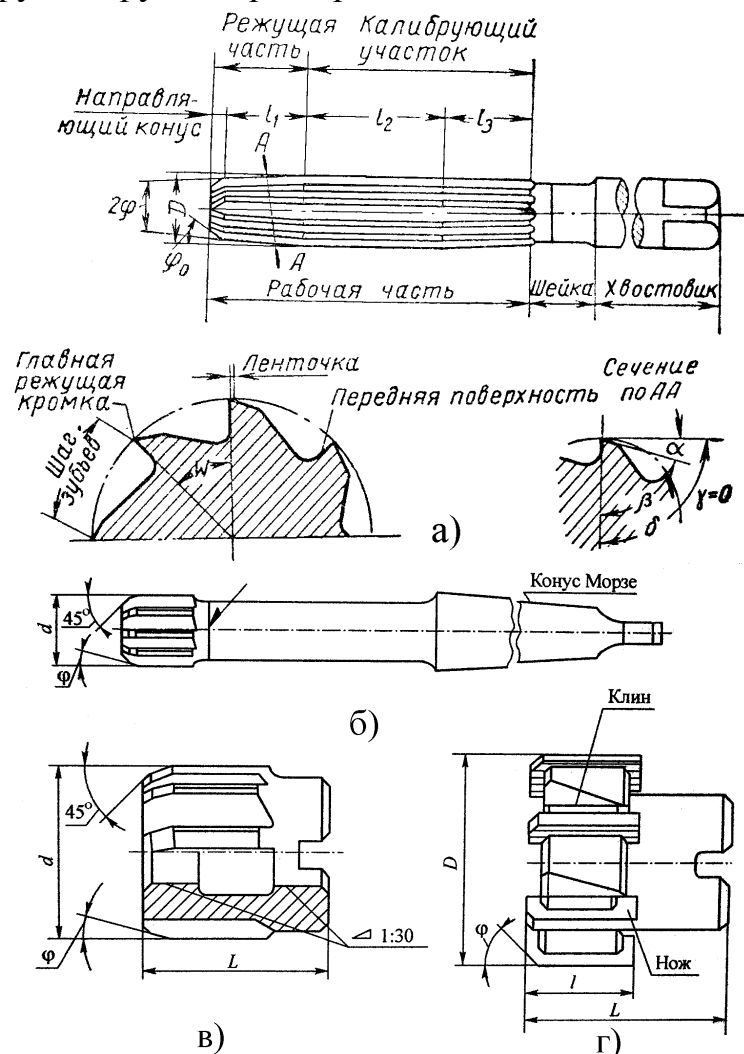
Типы разверток с основными частями: а – ручная; б – машинная; в – насадная; г – сборная.
